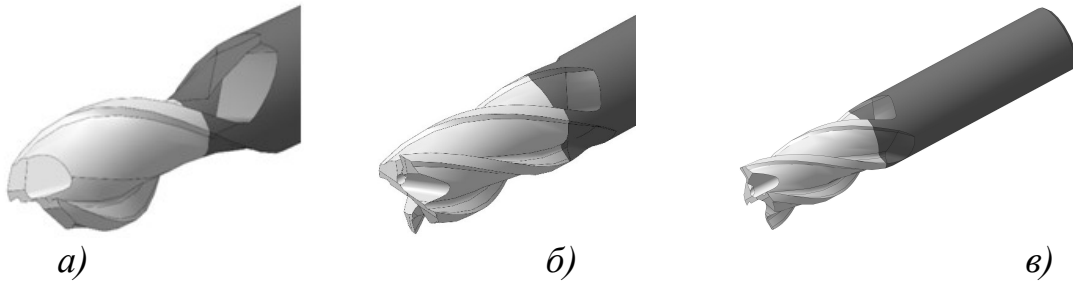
3D–модели фрез: с двумя режущими зубьями (а); с увеличенным диаметром (б); с углом винтовой канавки равной 38°
